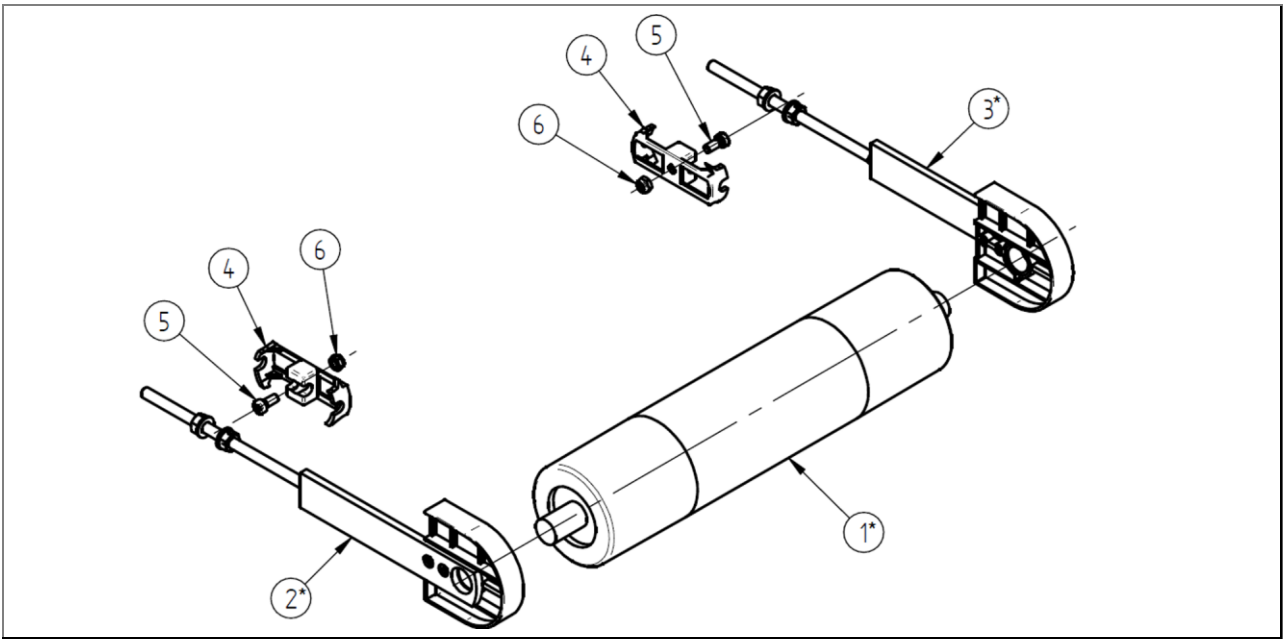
Lista de piezas: Unidad de retorno Multi-Tech Ø80– ZZ.800.0093.03
